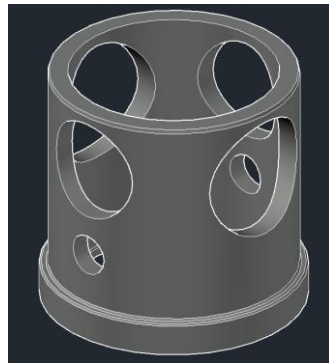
Estrutura interna da válvula modelada em AutoCAD.
